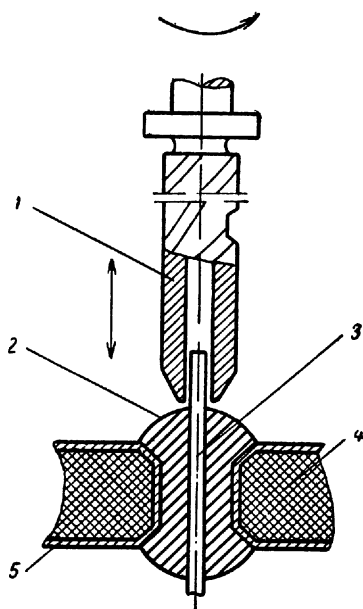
Зачистка монтажного отверстия печатной платы с помощью полый фрезы:
